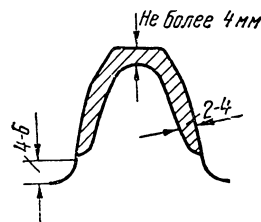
Расположение закаленной зоны на зубе ведомого зубчатого колеса (при накатке впадины зуба роликом)
